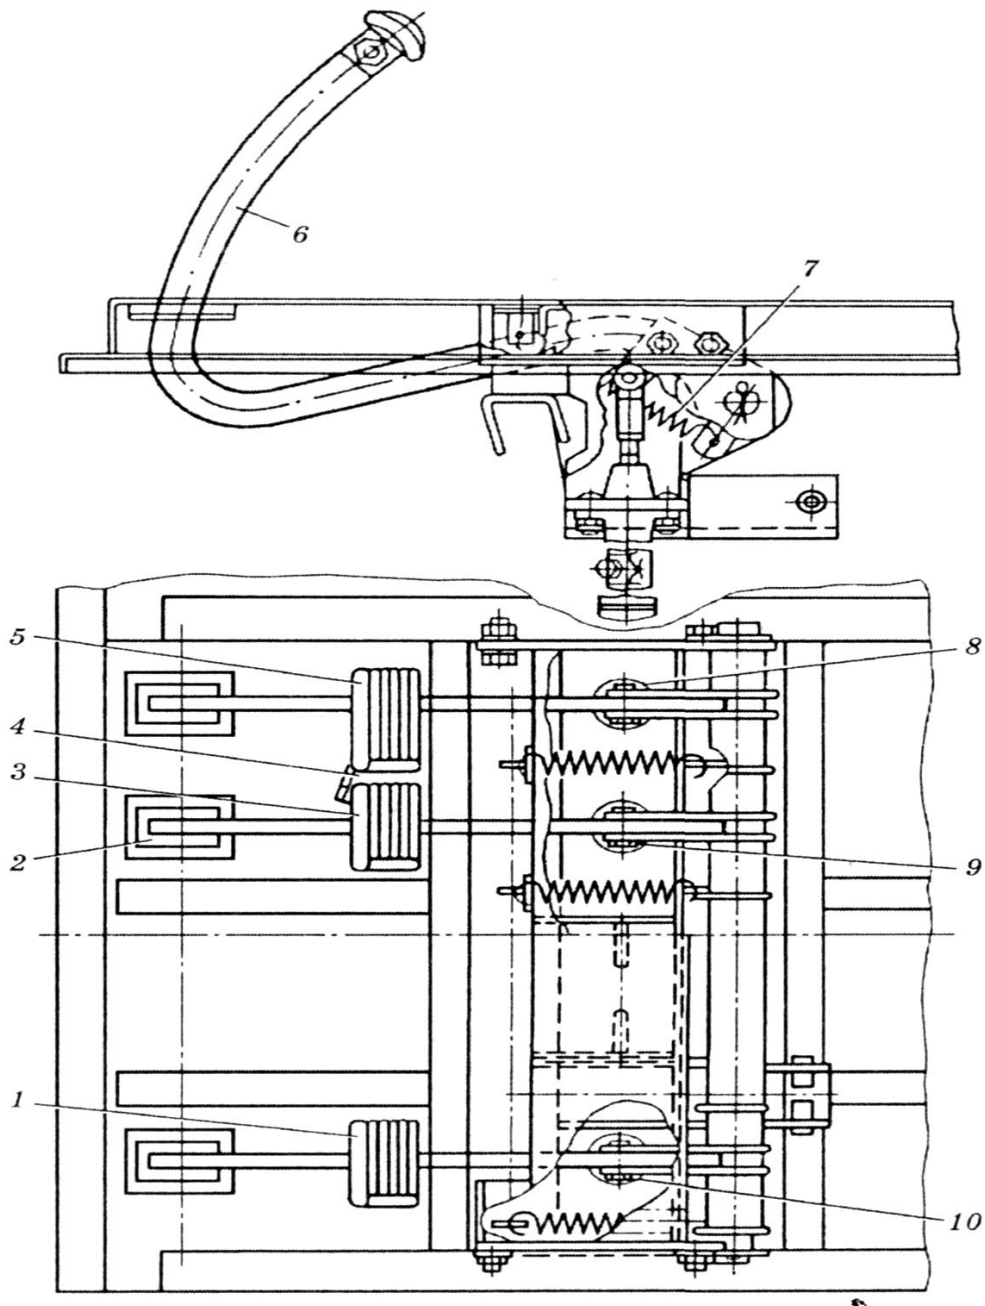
Пристрій керування гальмівними механізмами ведучих коліс зернозбирального комбайна «Дон-1500»:
